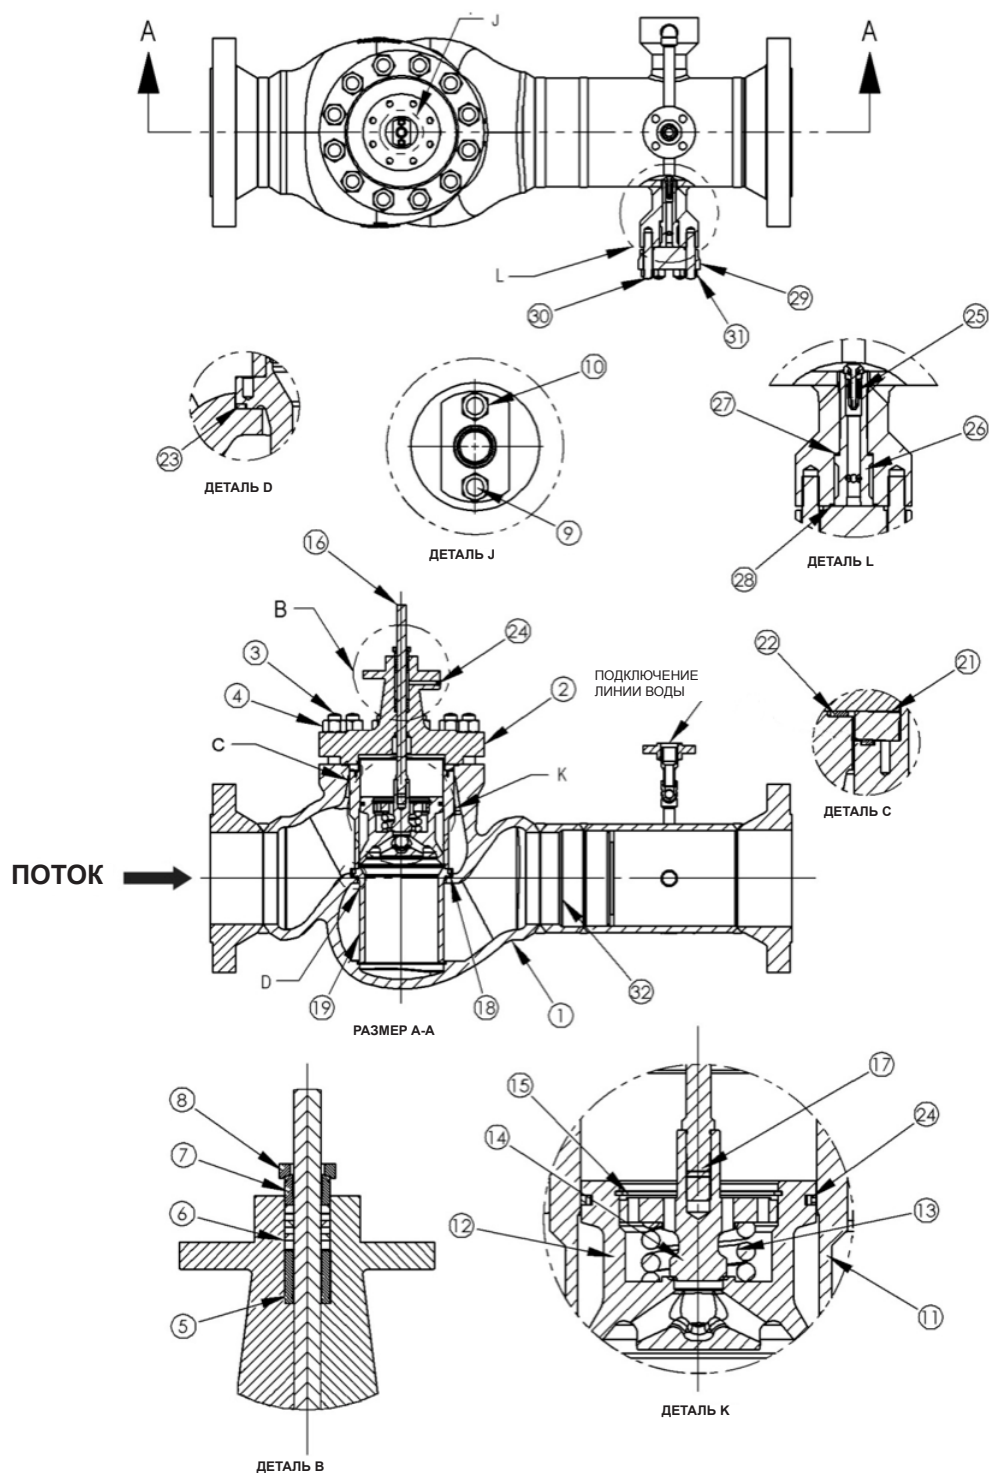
3-ступенчатый корпус шарового клапана SteamForm с конструкцией пробки с управляющим клапаном, вставным диффузором второй ступени и шумозащитной пластиной для ступени 3.
